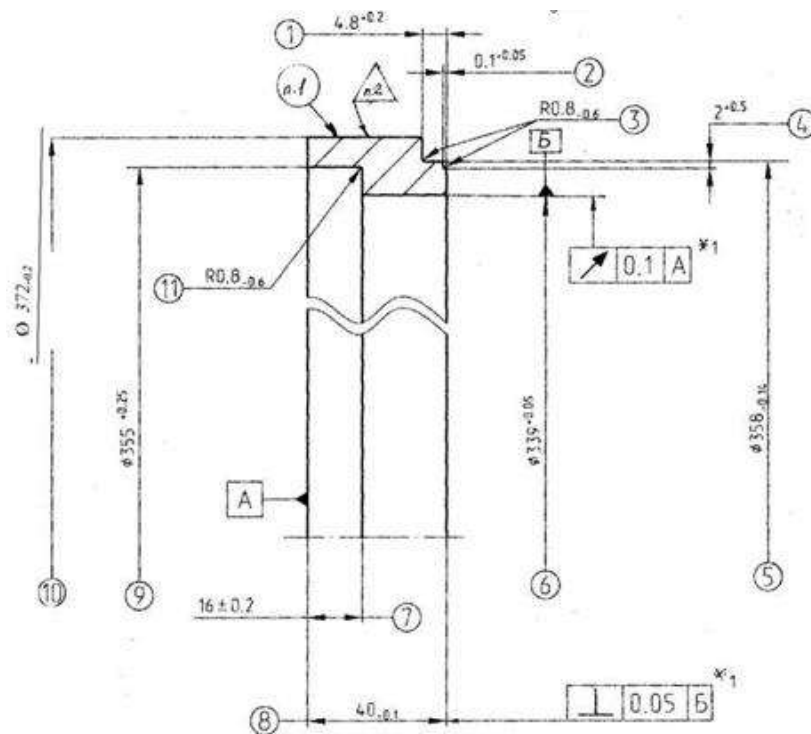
Механічно оброблена заготовка 1001-6601 під зварювання ЕПЗ.
